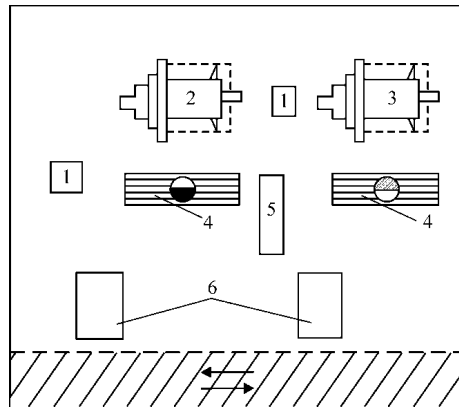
Робоче місце фрезерувальника (площа 40,1 м²): 1 – короб для стружки; 2 – вертикально-фрезерний верстат; 3 – горизонтально-фрезерний верстат; 4 – підставка-решітка; 5 – тумбочка для інструменту; 6 – стелаж для деталей.
